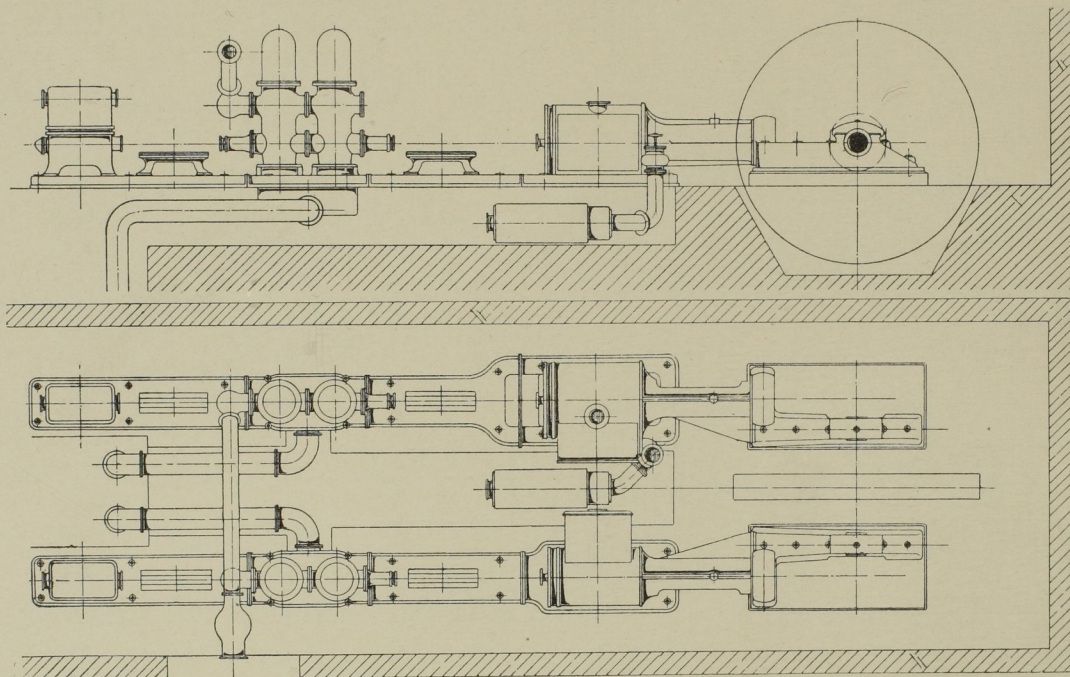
Seitenansicht und Grundriss der Maschine. Masst. 1:100.
